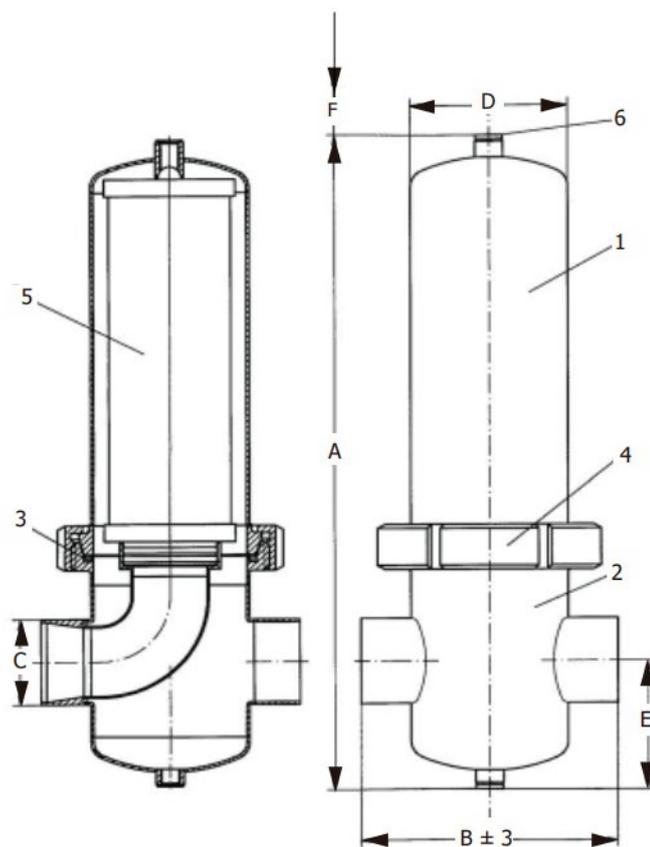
Корпус фильтров типа CSF-H моделей 0006-0288 с соединением под приварку.
